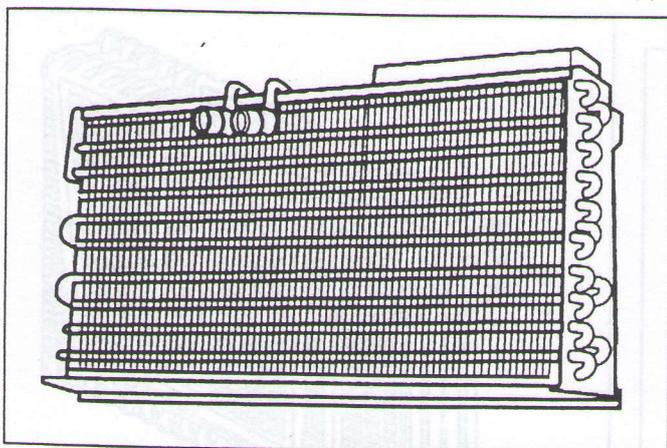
Конденсатор ребристо-трубчатый с пластинчатыми ребрами.
